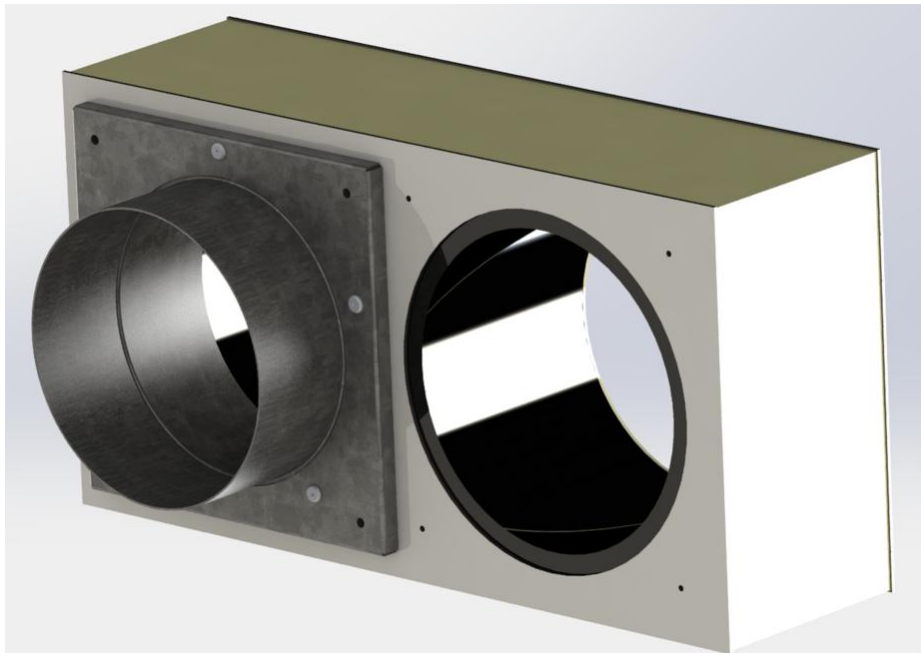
Разметка отверстий крепления фланцев наружной стенки.
